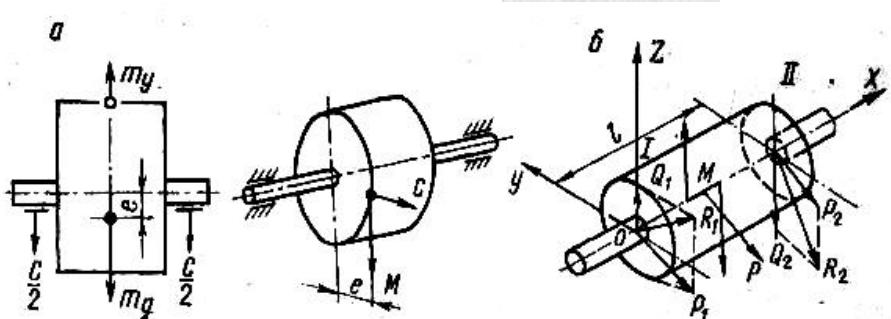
Дисбаланс ротора: а — статический; б — динамический
